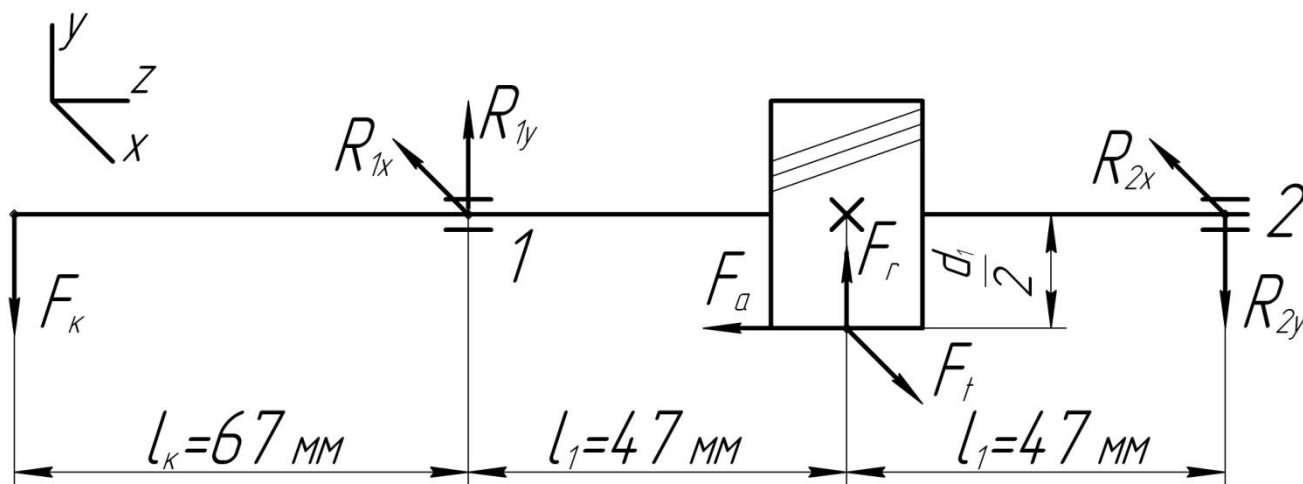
Расчётная схема ведущего вала редуктора.
